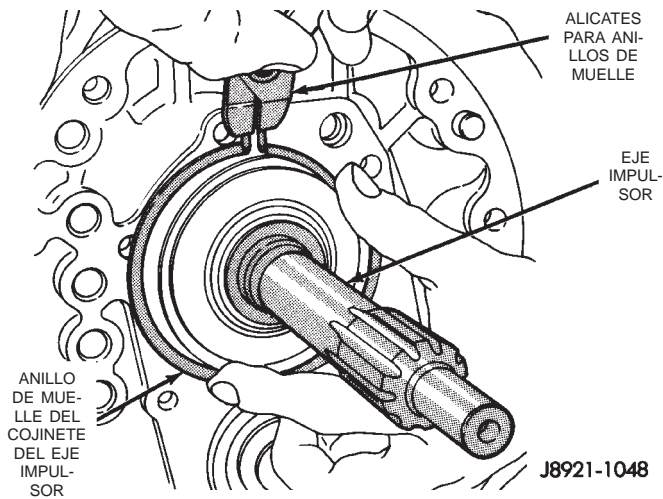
Desmontaje del anillo de muelle del cojinete del eje impulsor
